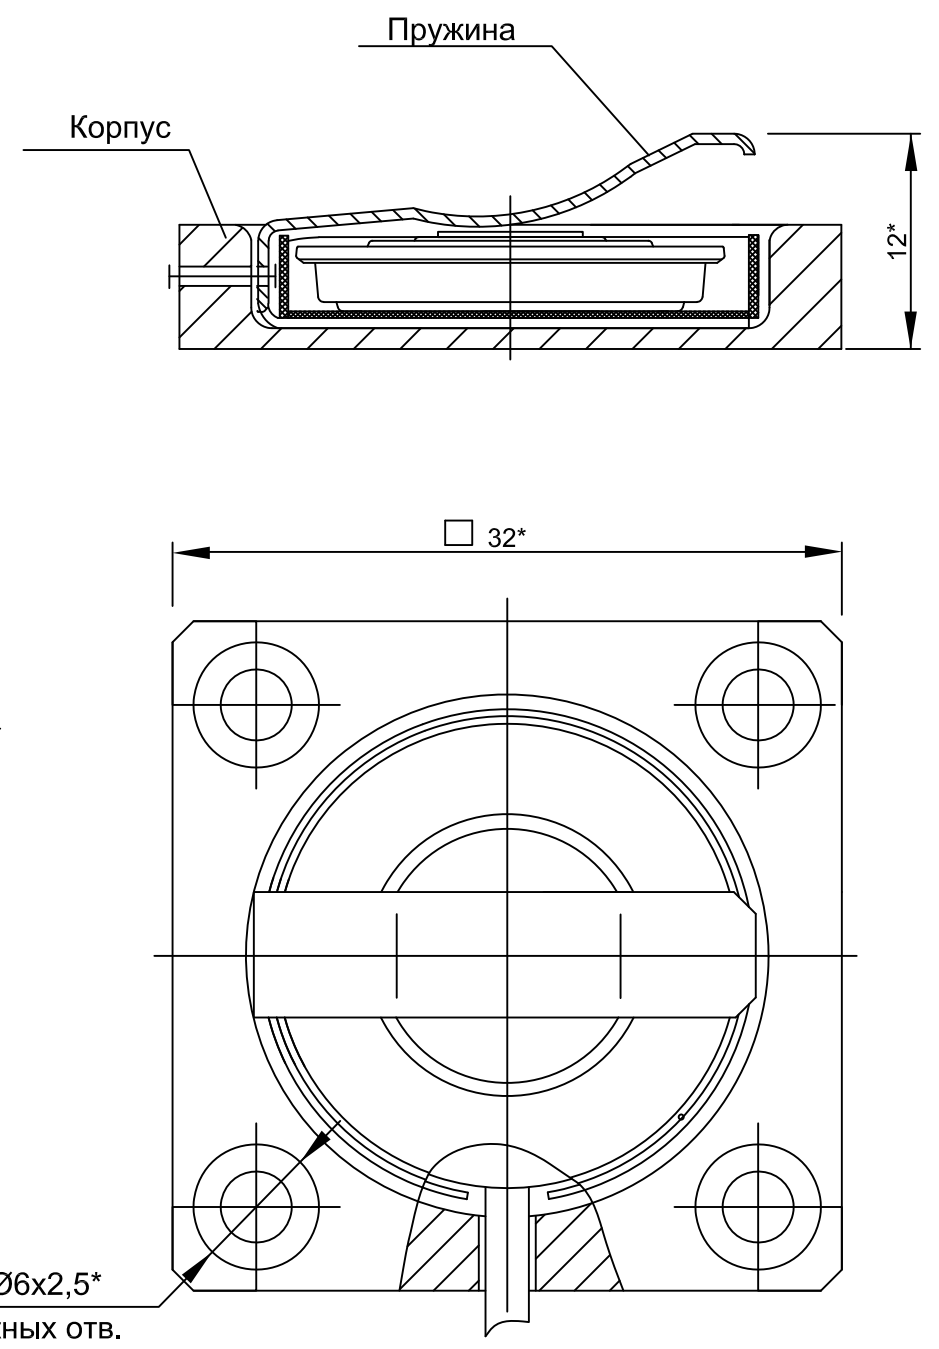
Габаритные размеры сенсора СПП-1Г2
